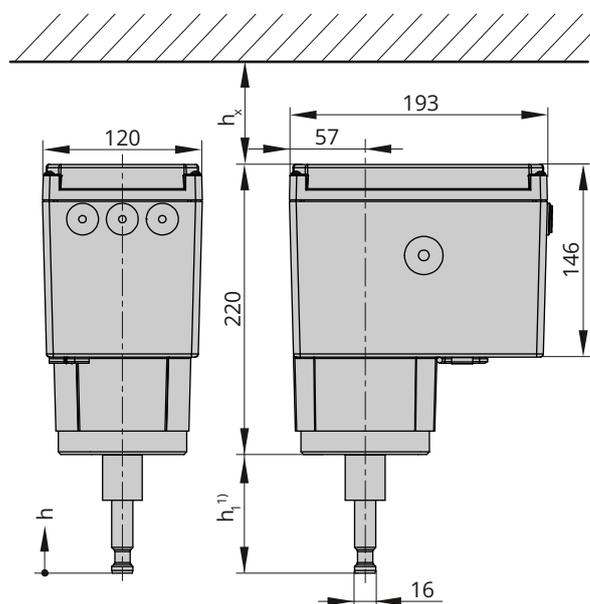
Maße in mm · Typ 3374-15, -17, -26 und -36, (Form A)
